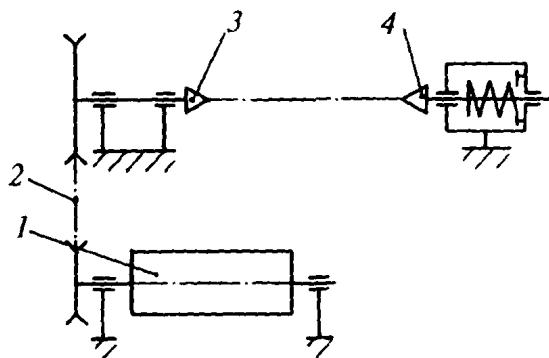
Схема стана для газопорошковой наплавки кулачков распределительного вала:
